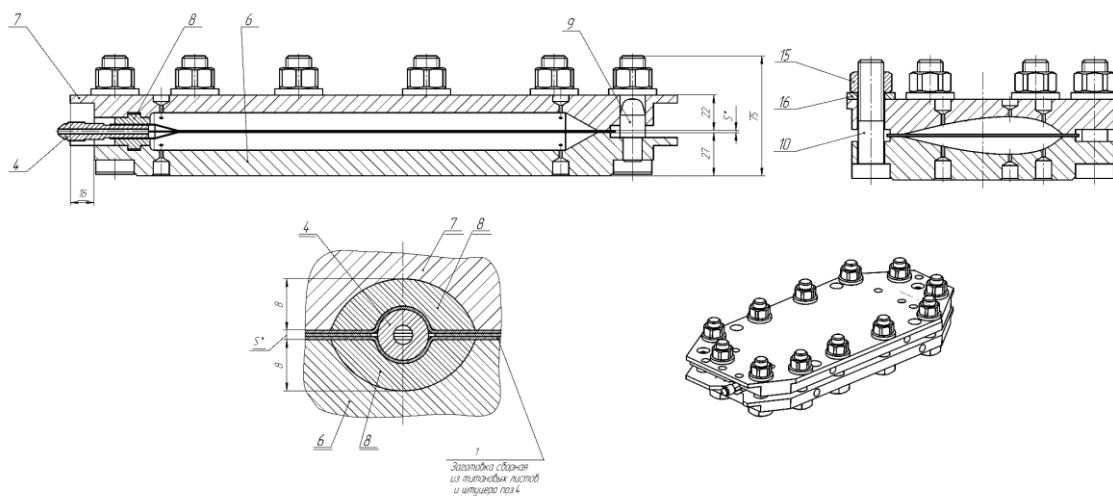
Оснащення для виготовлення елементу порожнистої лопатки
